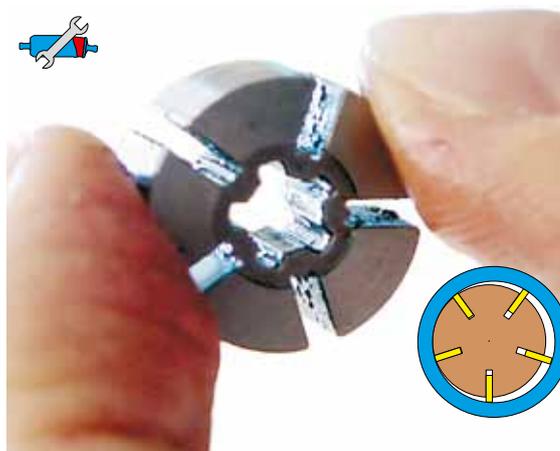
Meccanismo di pompaggio sporco di una pompa a palette
